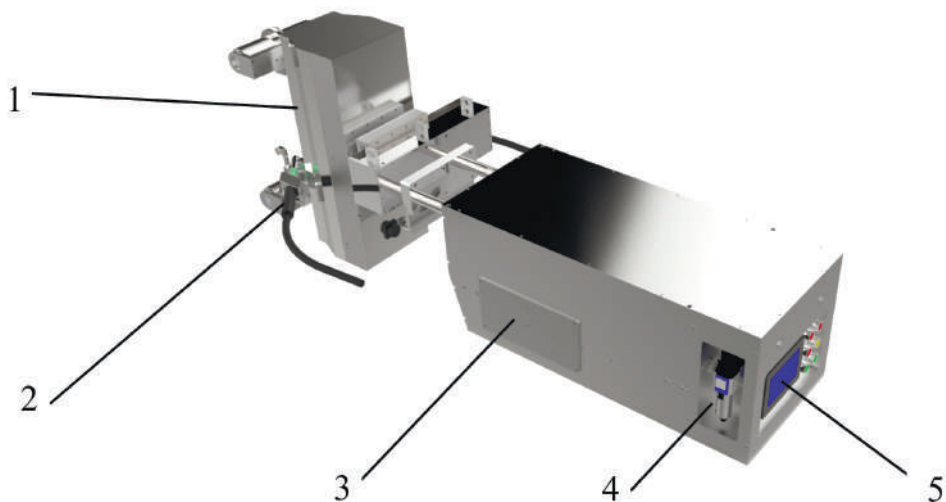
а. Схема устройства автоматического сварочного робота: 1 – сварочная головка, 2 – сварочная горелка, 3 – смотровое окно, 4 – манометр, 5 – панель управления
